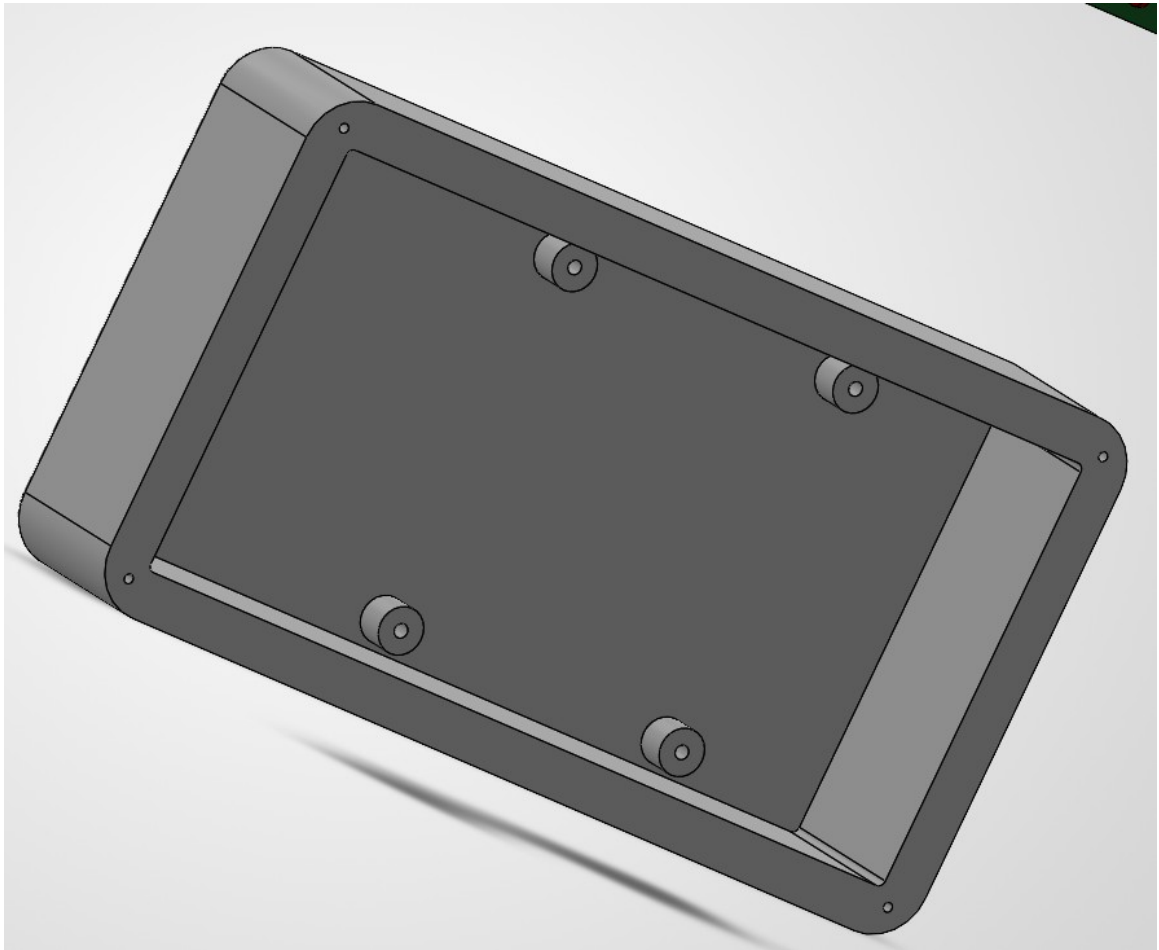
Нижня кришка корпусу, ізометричний вигляд
